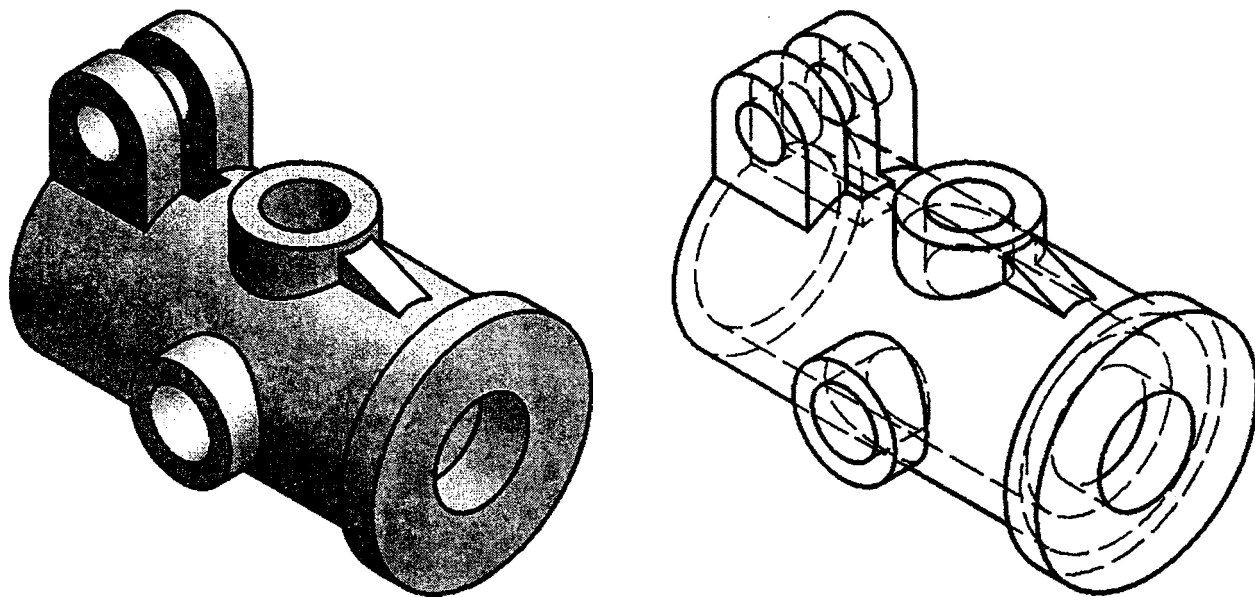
Образец детали сложной геометрической формы (к чертежу на рис. 3.16)
